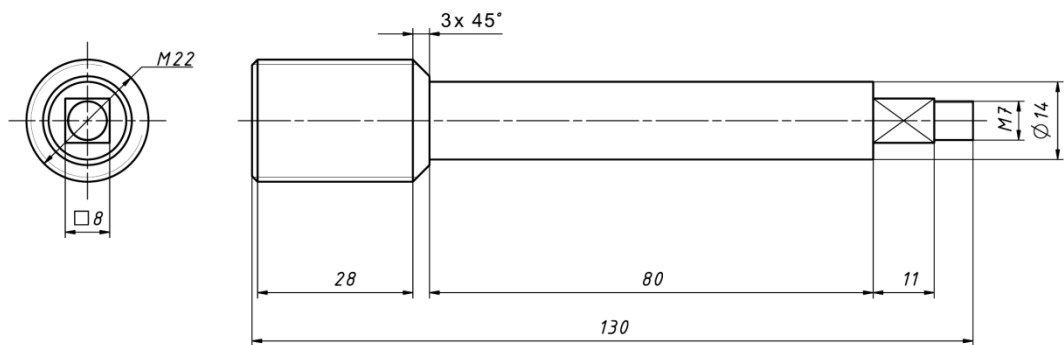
Пример оформления сборочного чертежа для задания 3
